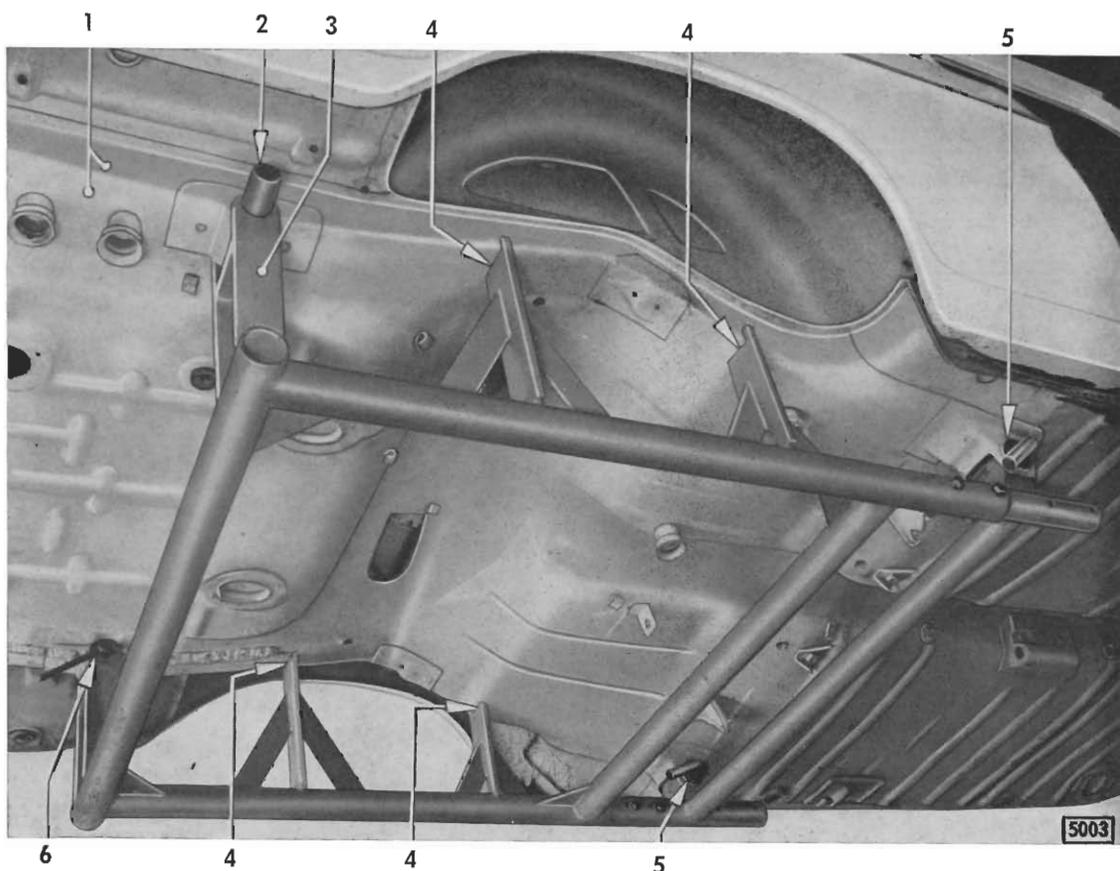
Kofferraumbodenprofil an Hinterlängsträger-Schweißlehre angepaßt
